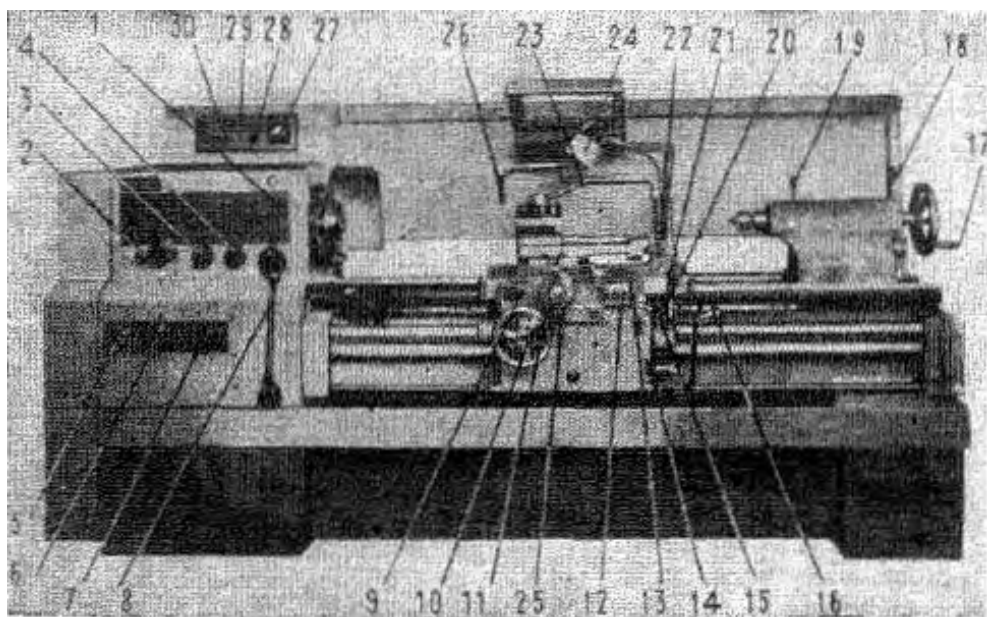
Органи керування токарно – гвинторізного верстата
